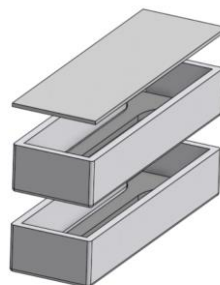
Vue éclatée du dispositif en alumine (deux creusets et une plaque)
